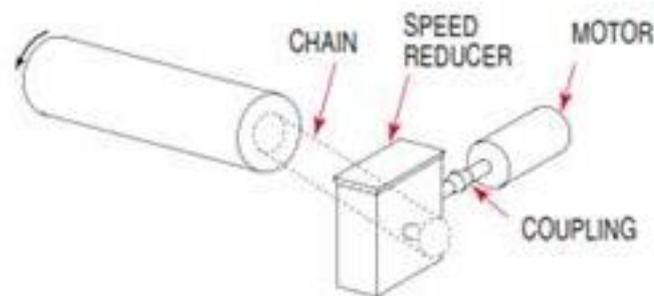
10 Roller Conveyor (DM Prabowo, 2018)
